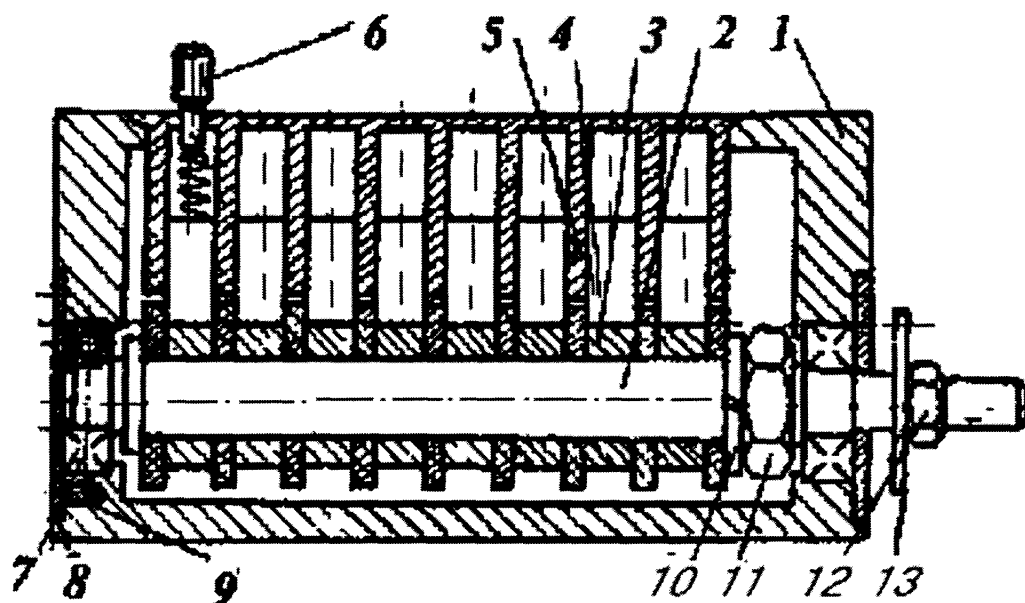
Щітковий струмознімач: 1 – корпус; 2 – валик; 3 – мідні кільця; 4 – графітні щітки; 5 – перегородка корпусу; 6 – регулювальні гвинти; 7 – вальниці кочення; 8 – кришка; 9 – циліндричні пружини; 10, 12 – шайби; 11, 13 – гайки
